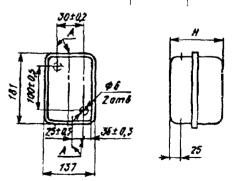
Габаритные, установочные размеры пускателей типа ПМ12-010 реверсивных в оболочках степени защиты IP40
